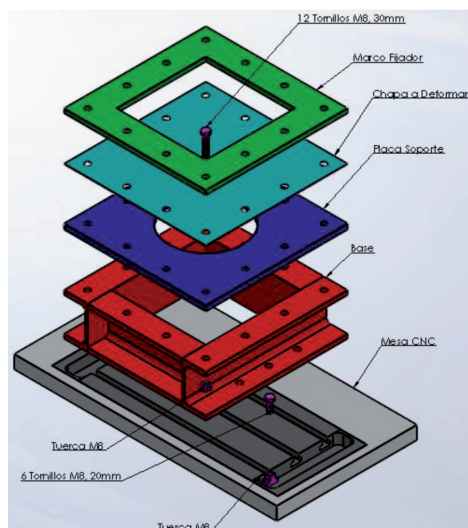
Conjunto explosionado del bastidor de fijación, diseñado y fabricado para realizar los ensayos
